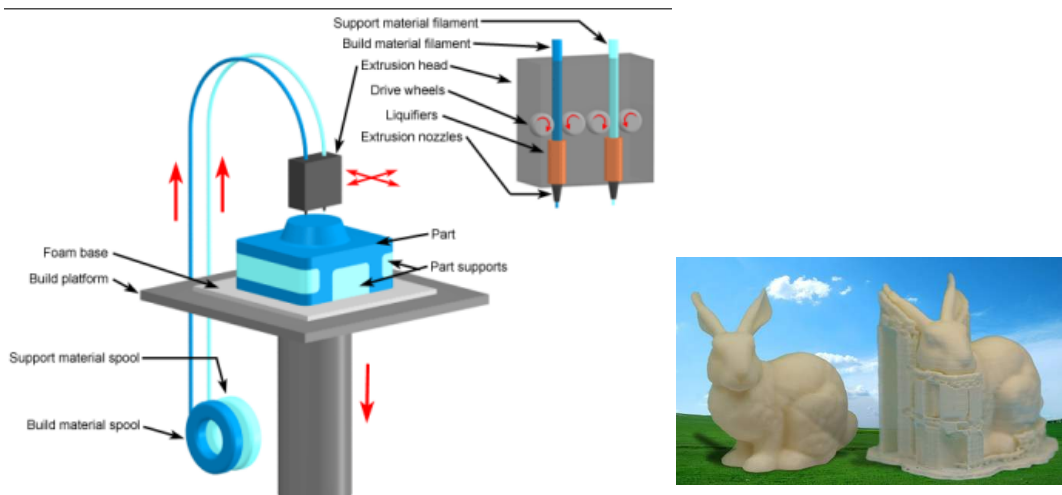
Imatge impressora 3d d'extrusió doble. La figura impresa queda suportada pel material de suport (color blau clar esquerra).
